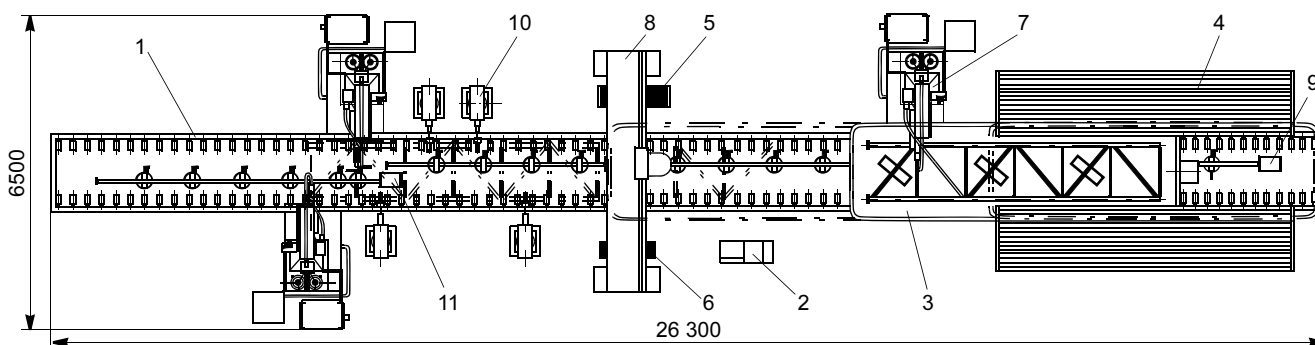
Автоматическая сборочно-сварочная линия для производства ферм мачтовых сооружений
